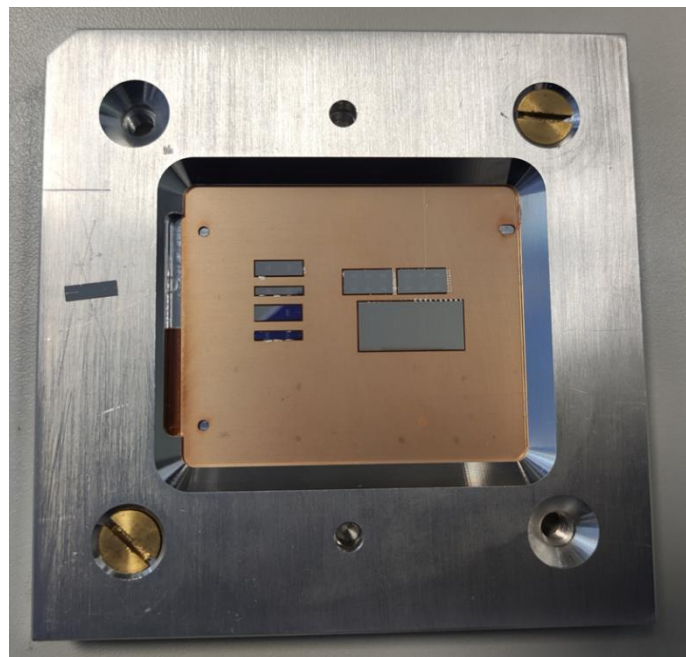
Halterung für die Bestückung der Chips auf PCB.
